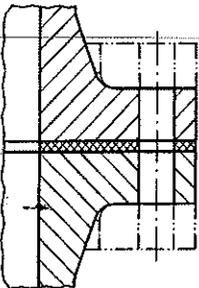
Vorschweißflansch mit durchgehender Dichtung und Metall-Losflansch
